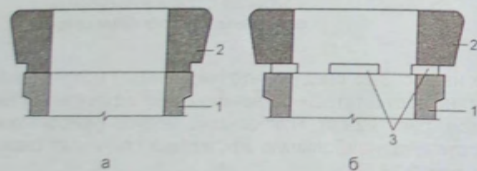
Схемы разрезов моделей кольцевых прибылей: 1 — отливка; 2 — прибыль; 3 — "окна" в шейке прибыли
